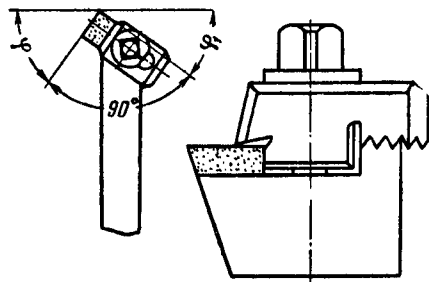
Резец с механическим креплением пластинки твёрдого сплава
